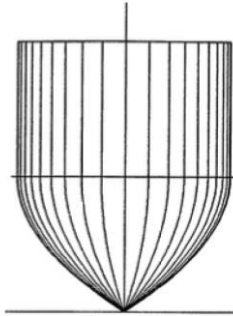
Теоретичне креслення корпусу тіла Виглей
